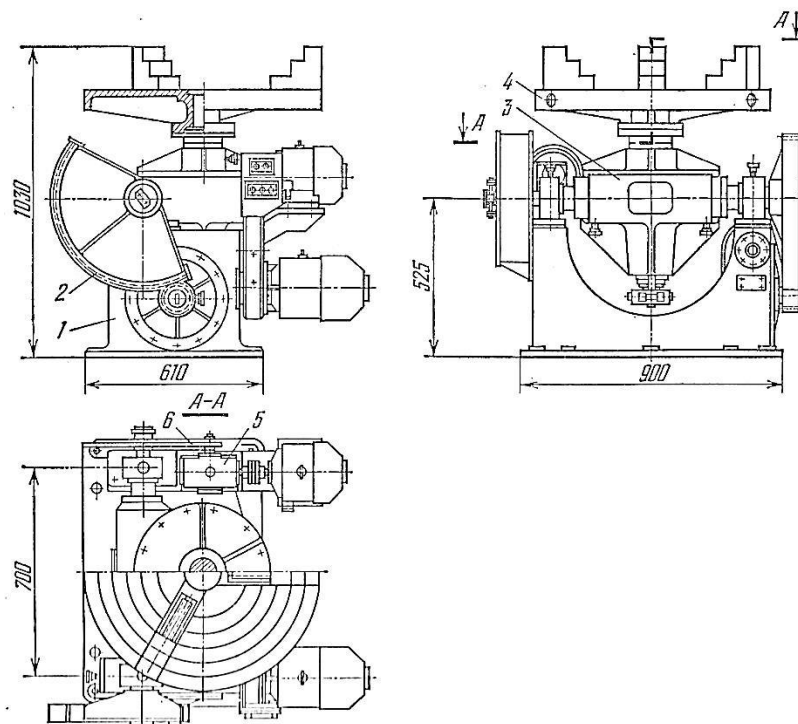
Зварювальний маніпулятор Т-25М: 1 – станина; 2 – механізм нахилу; 3 – поворотна траверса; 4 – планшайба; 5 – механізм обертання планшайби; 6 – змінні шестерні
